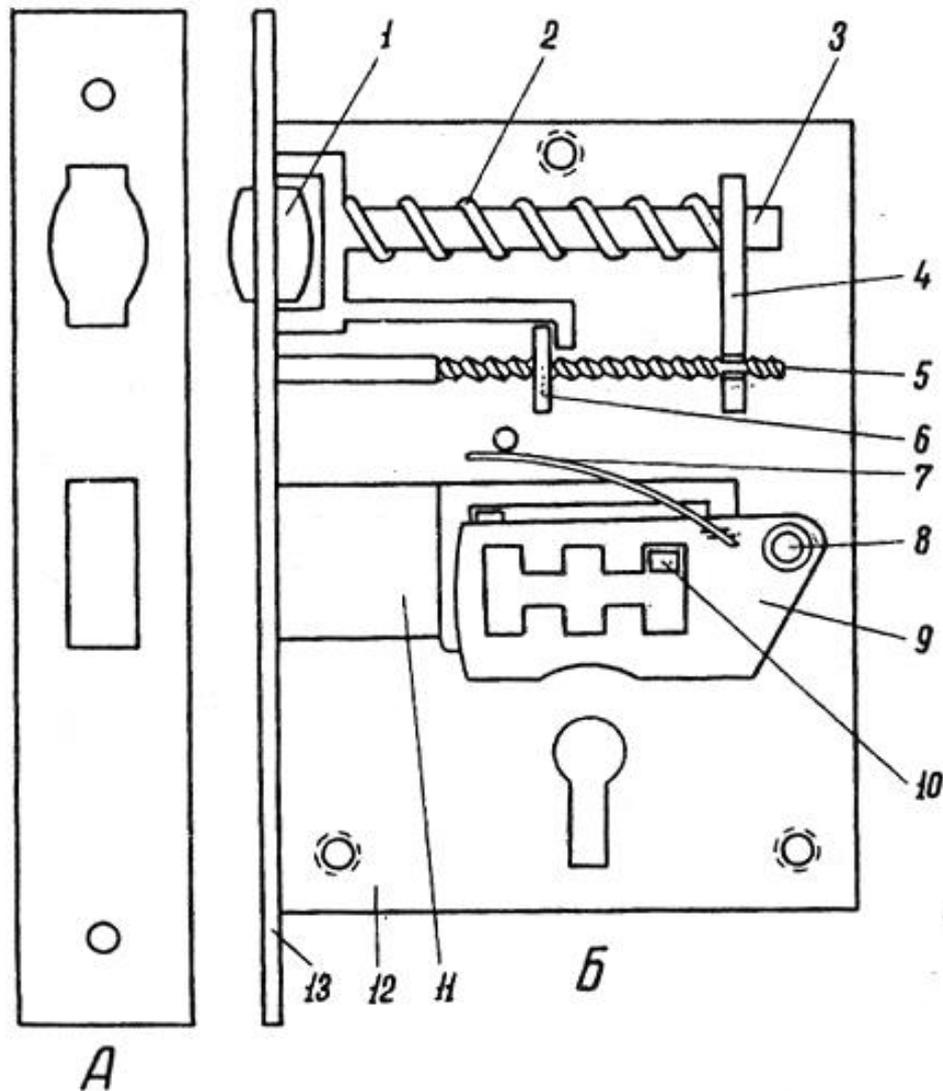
Устройство врезного дверного замка с сувальдным механизмом: А — запорная планка; Б — замок; 1 — ролик фиксатора; 2 — пружина; 3 — вилка; 4 — упорная планка; 5 — регулировочный винт; 6 — регулировочная планка (гайка винта); 7 — пружина сувальды; 8 — ось сувальды; 9 — сувальда; 10 — стойка засова; 11 — засов; 12 — основание корпуса; 13 — лицевая планка
